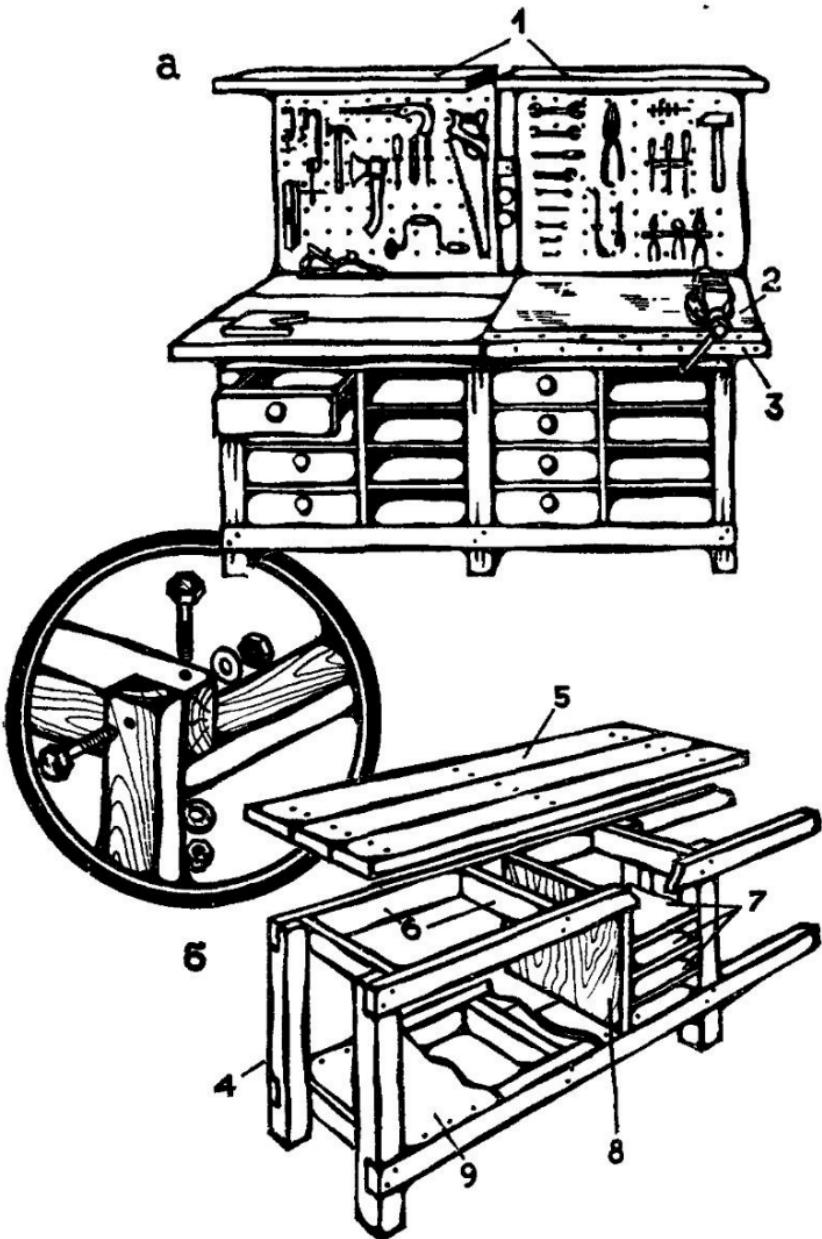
Универсальный рабочий стол (а) и детали конструкции рабочего стола (б).
